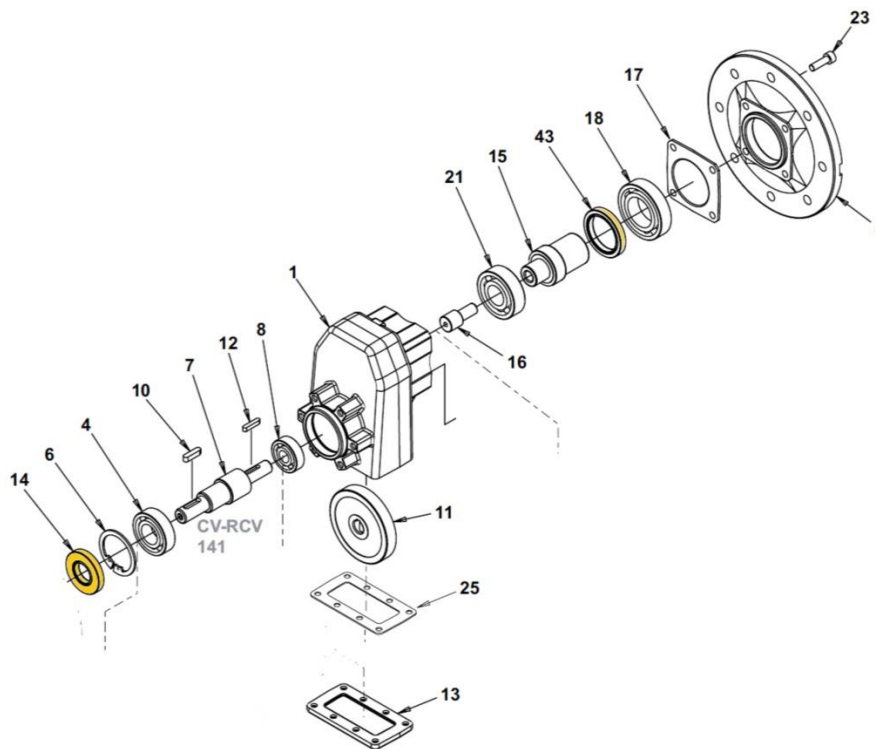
Explosionszeichnung des verwendeten Getriebes. Die Wellendichtringe sind gelb hervorgehoben. [14]
